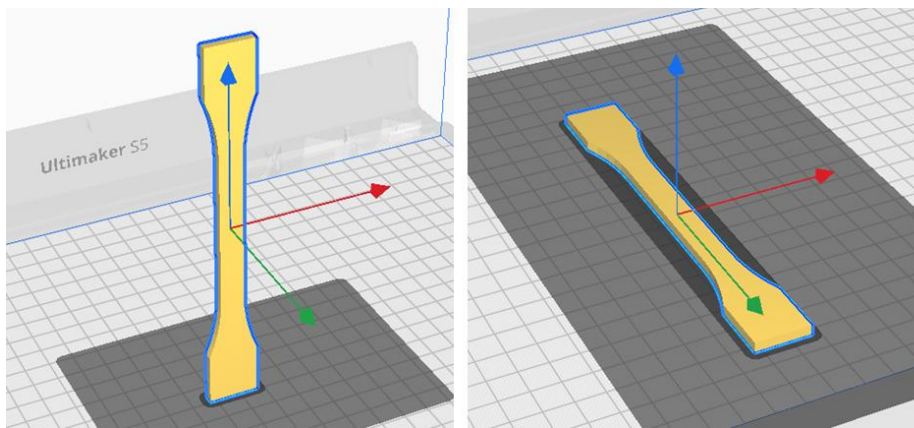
Orientação de construção: a) Vertical; b) Horizontal
